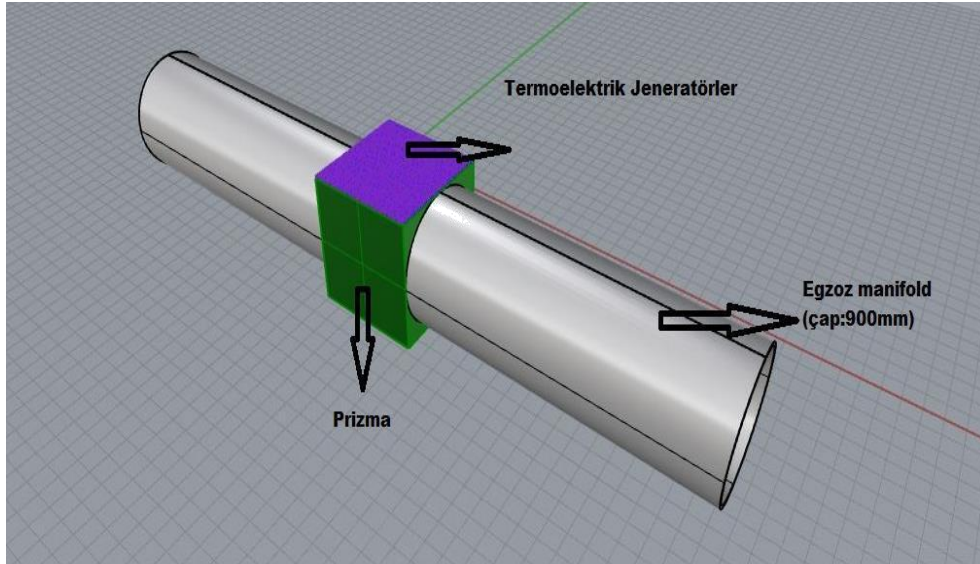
Ana makine egzoz manifold – turbo inlet, outlet
